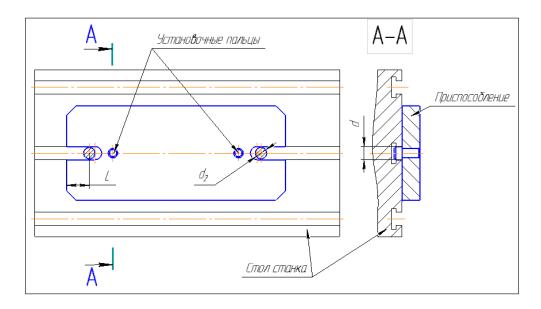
Базирование на столе станка с помощью сменных пальцев или шпонок с закреплением болтами
